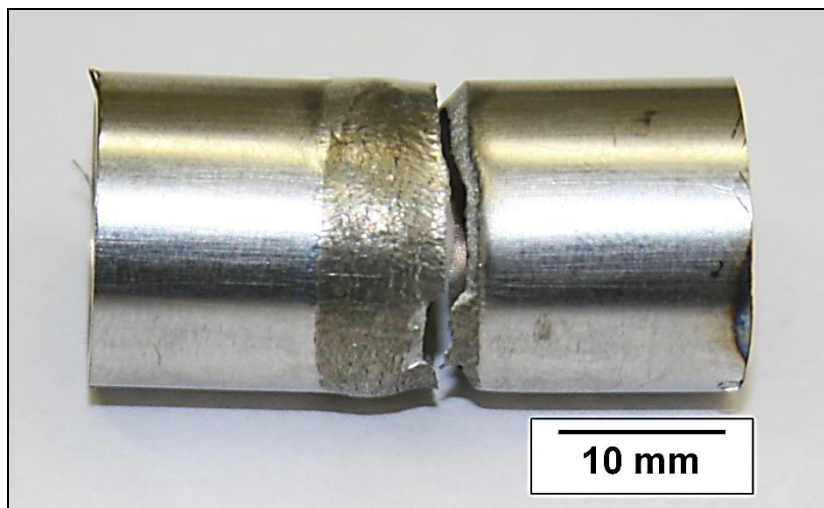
Corpo de prova soldado e hydrogenado com surgimento de trincas secundárias no cordão de solda.
